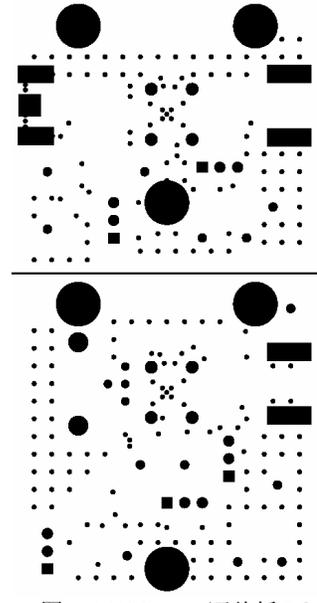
MAX3654 评估板 PCB 布局—焊接层
